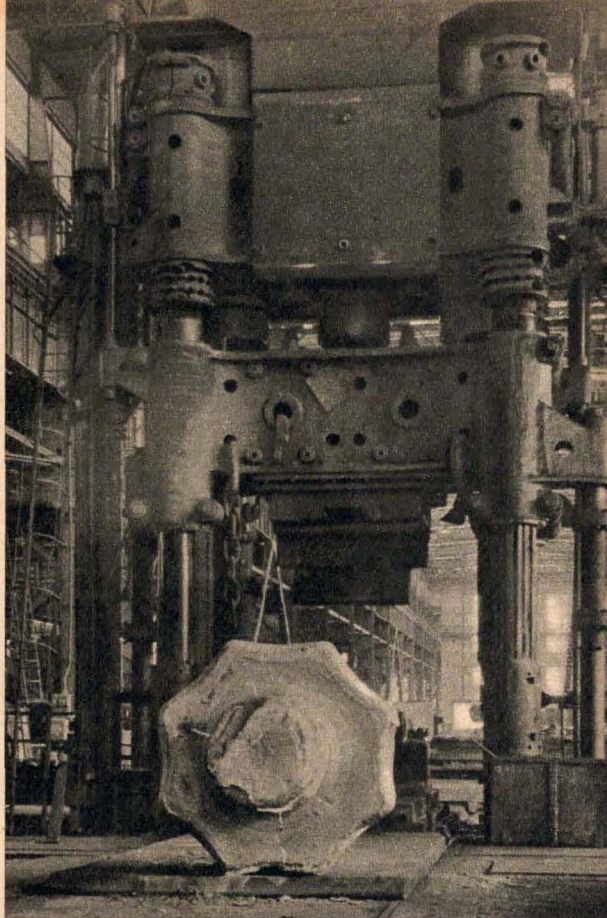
Freiformschmiedepresse mit einer Druckkraft von 6000 Mp.
